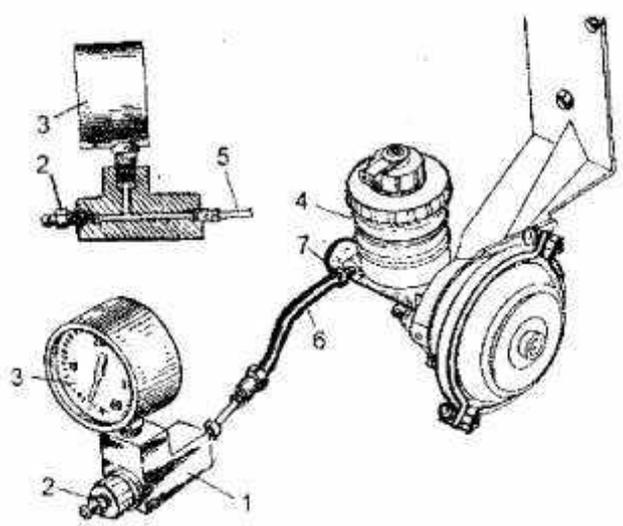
Приспособление для проверки главного тормозного цилиндра:
